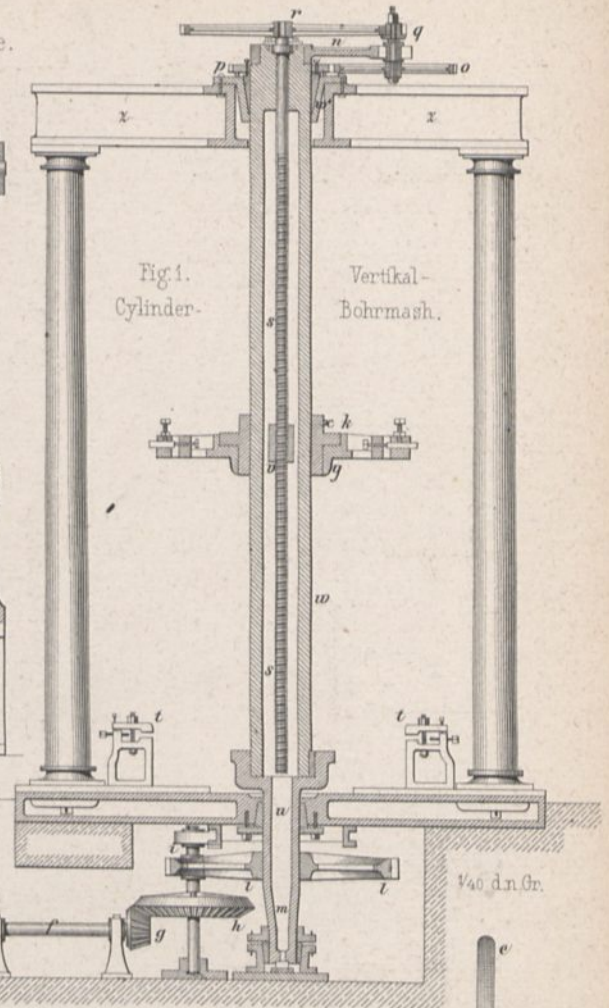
Cylinder-Bohrmaschine. Vertikal-Bohrmaschine.
